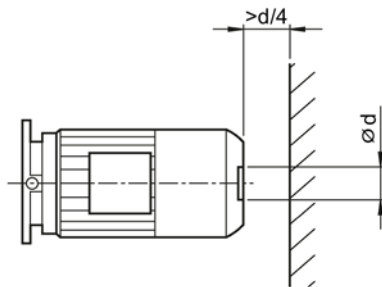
Aufstellbedingung für den MOTOX Motor
